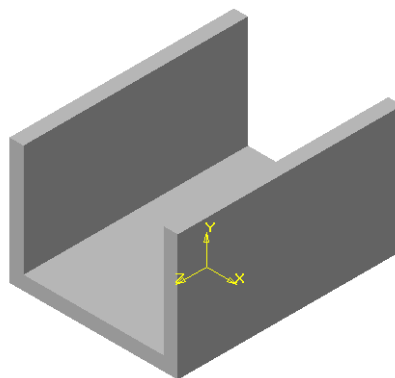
Тривимірна модель корпусу струбцини з новоствореними боковими елементами
